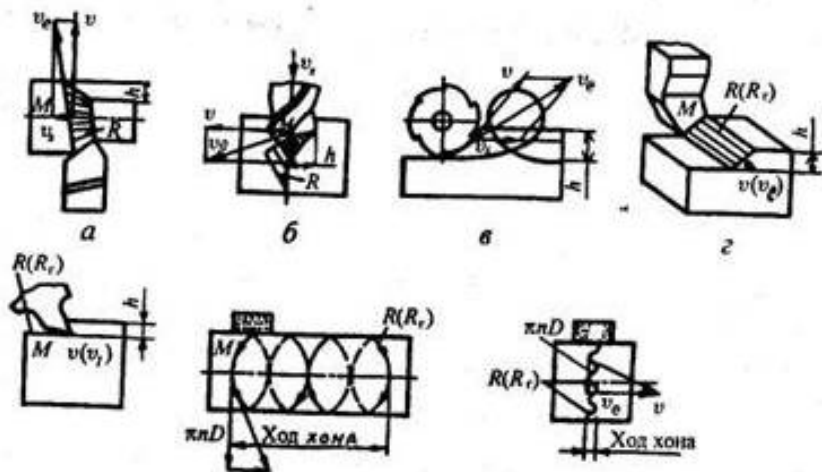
Схемы определения максимальной скорости режущей кромки инструмента v_e , формы поверхности резания R и глубины резания h при обработке:
